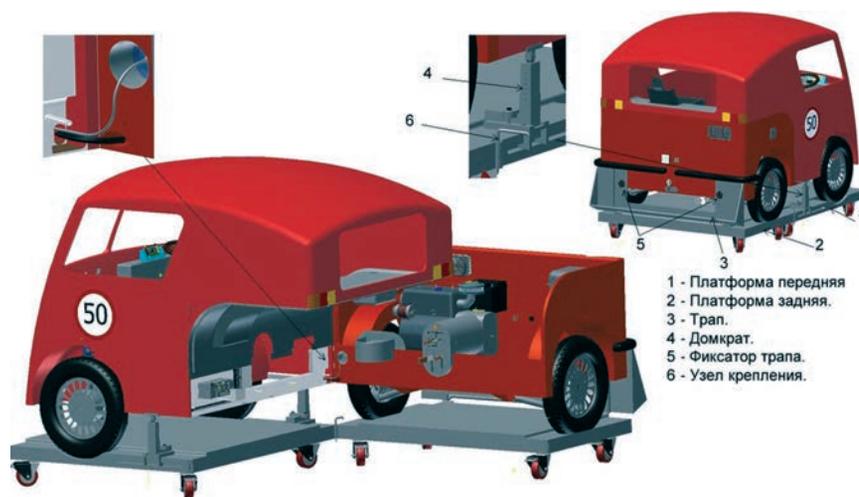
Стыковка и расстыковка кузова и мотоблока
